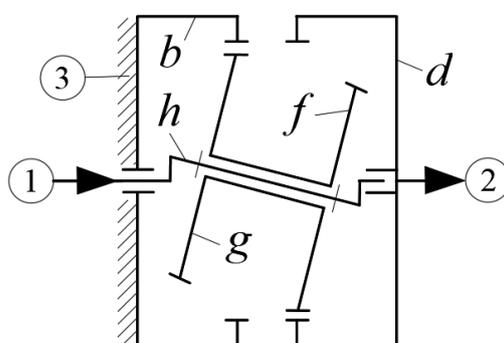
Прецессионный механизм с двухзвенцовым сателлитом
